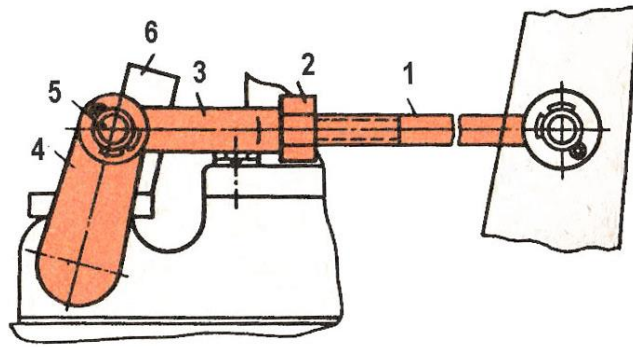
Регулювання механізму блокування перемикання діапазонів коробки передач трактора ХТЗ-17221
